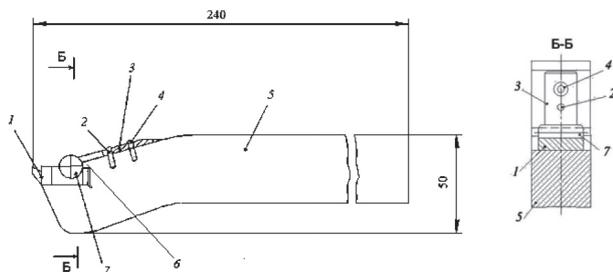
Специальный резец: 1 — режущий элемент; 2 — штифт; 3 — фиксирующая пластина; 4 — винт; 5 — державка; 6 — опора; 7 — цилиндрический валик
